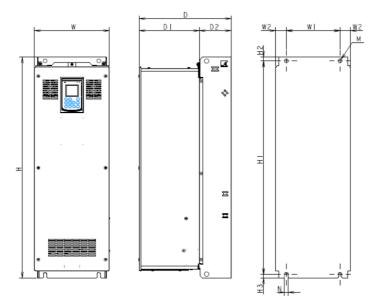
Dimensiones externas del variador (FRN45AQ1■-4□ a FRN90AQ1■-4□)
